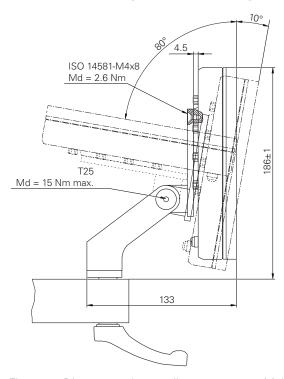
Dimensões do aparelho com suporte Multi-Pos
